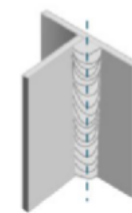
Soldadura en posición 3F (American Welding Society, 2018)
